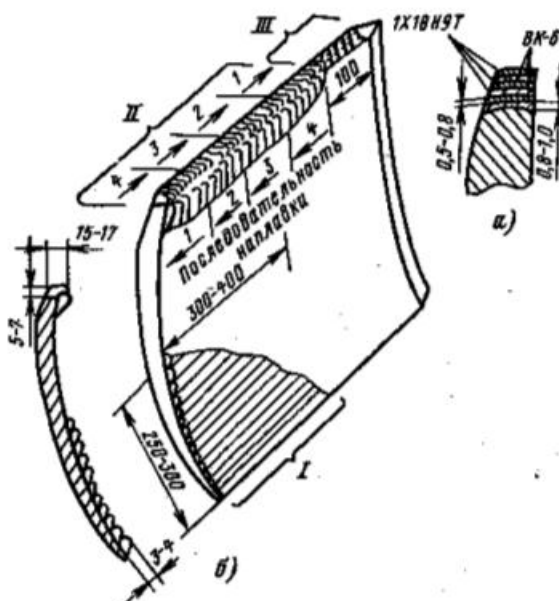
Схема наплавки запасной рабочей лопатки
